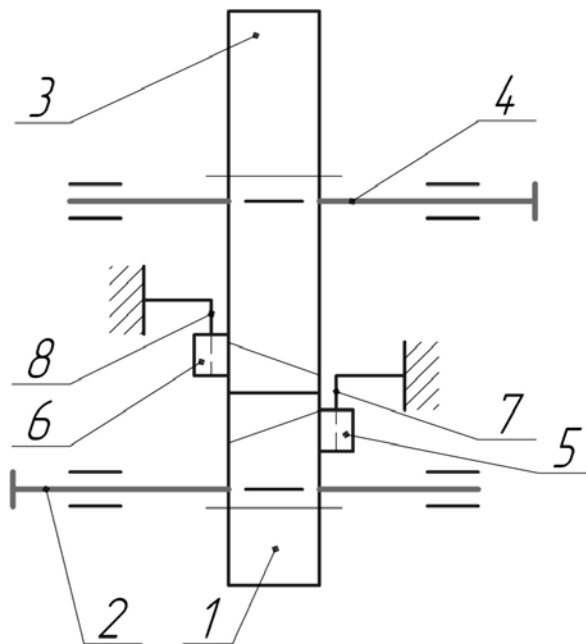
Схема косозубої передачі з роликівими компенсаторами осьових сил: 1 – шестерня; 2 – ведучий вал; 3 – зубчасте колесо; 4 – ведений вал; 5, 6 – циліндричні ролики; 7, 8 – осі роликів
